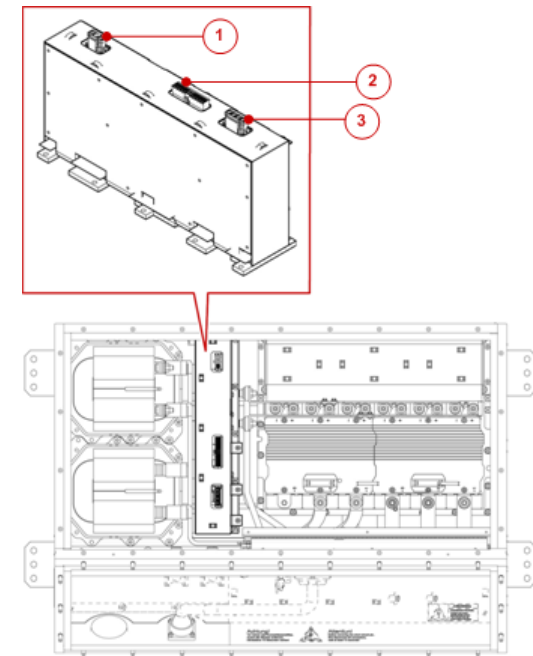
Explosionszeichnung Netzteil / Exploded view of power supply unit
